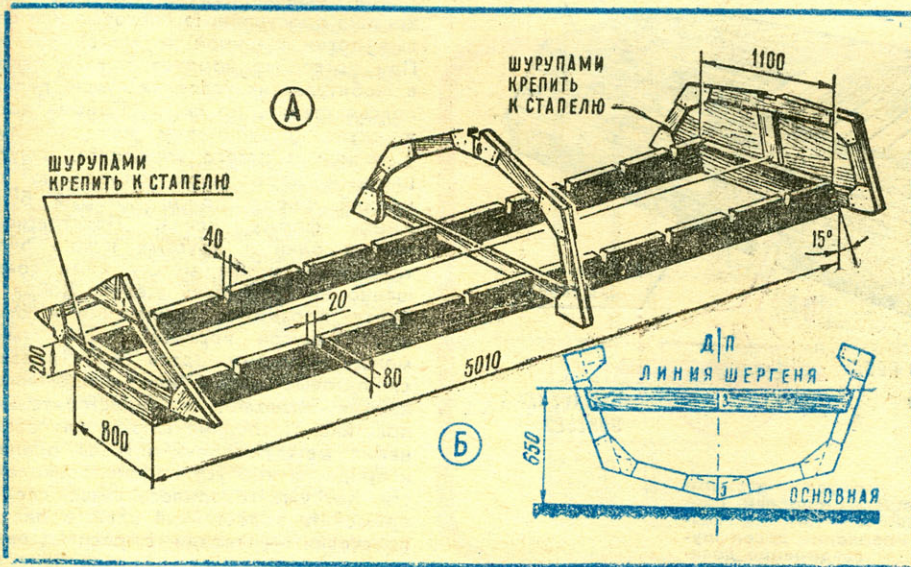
Рамный стапель для сборки корпуса и установка шпангоутов.
